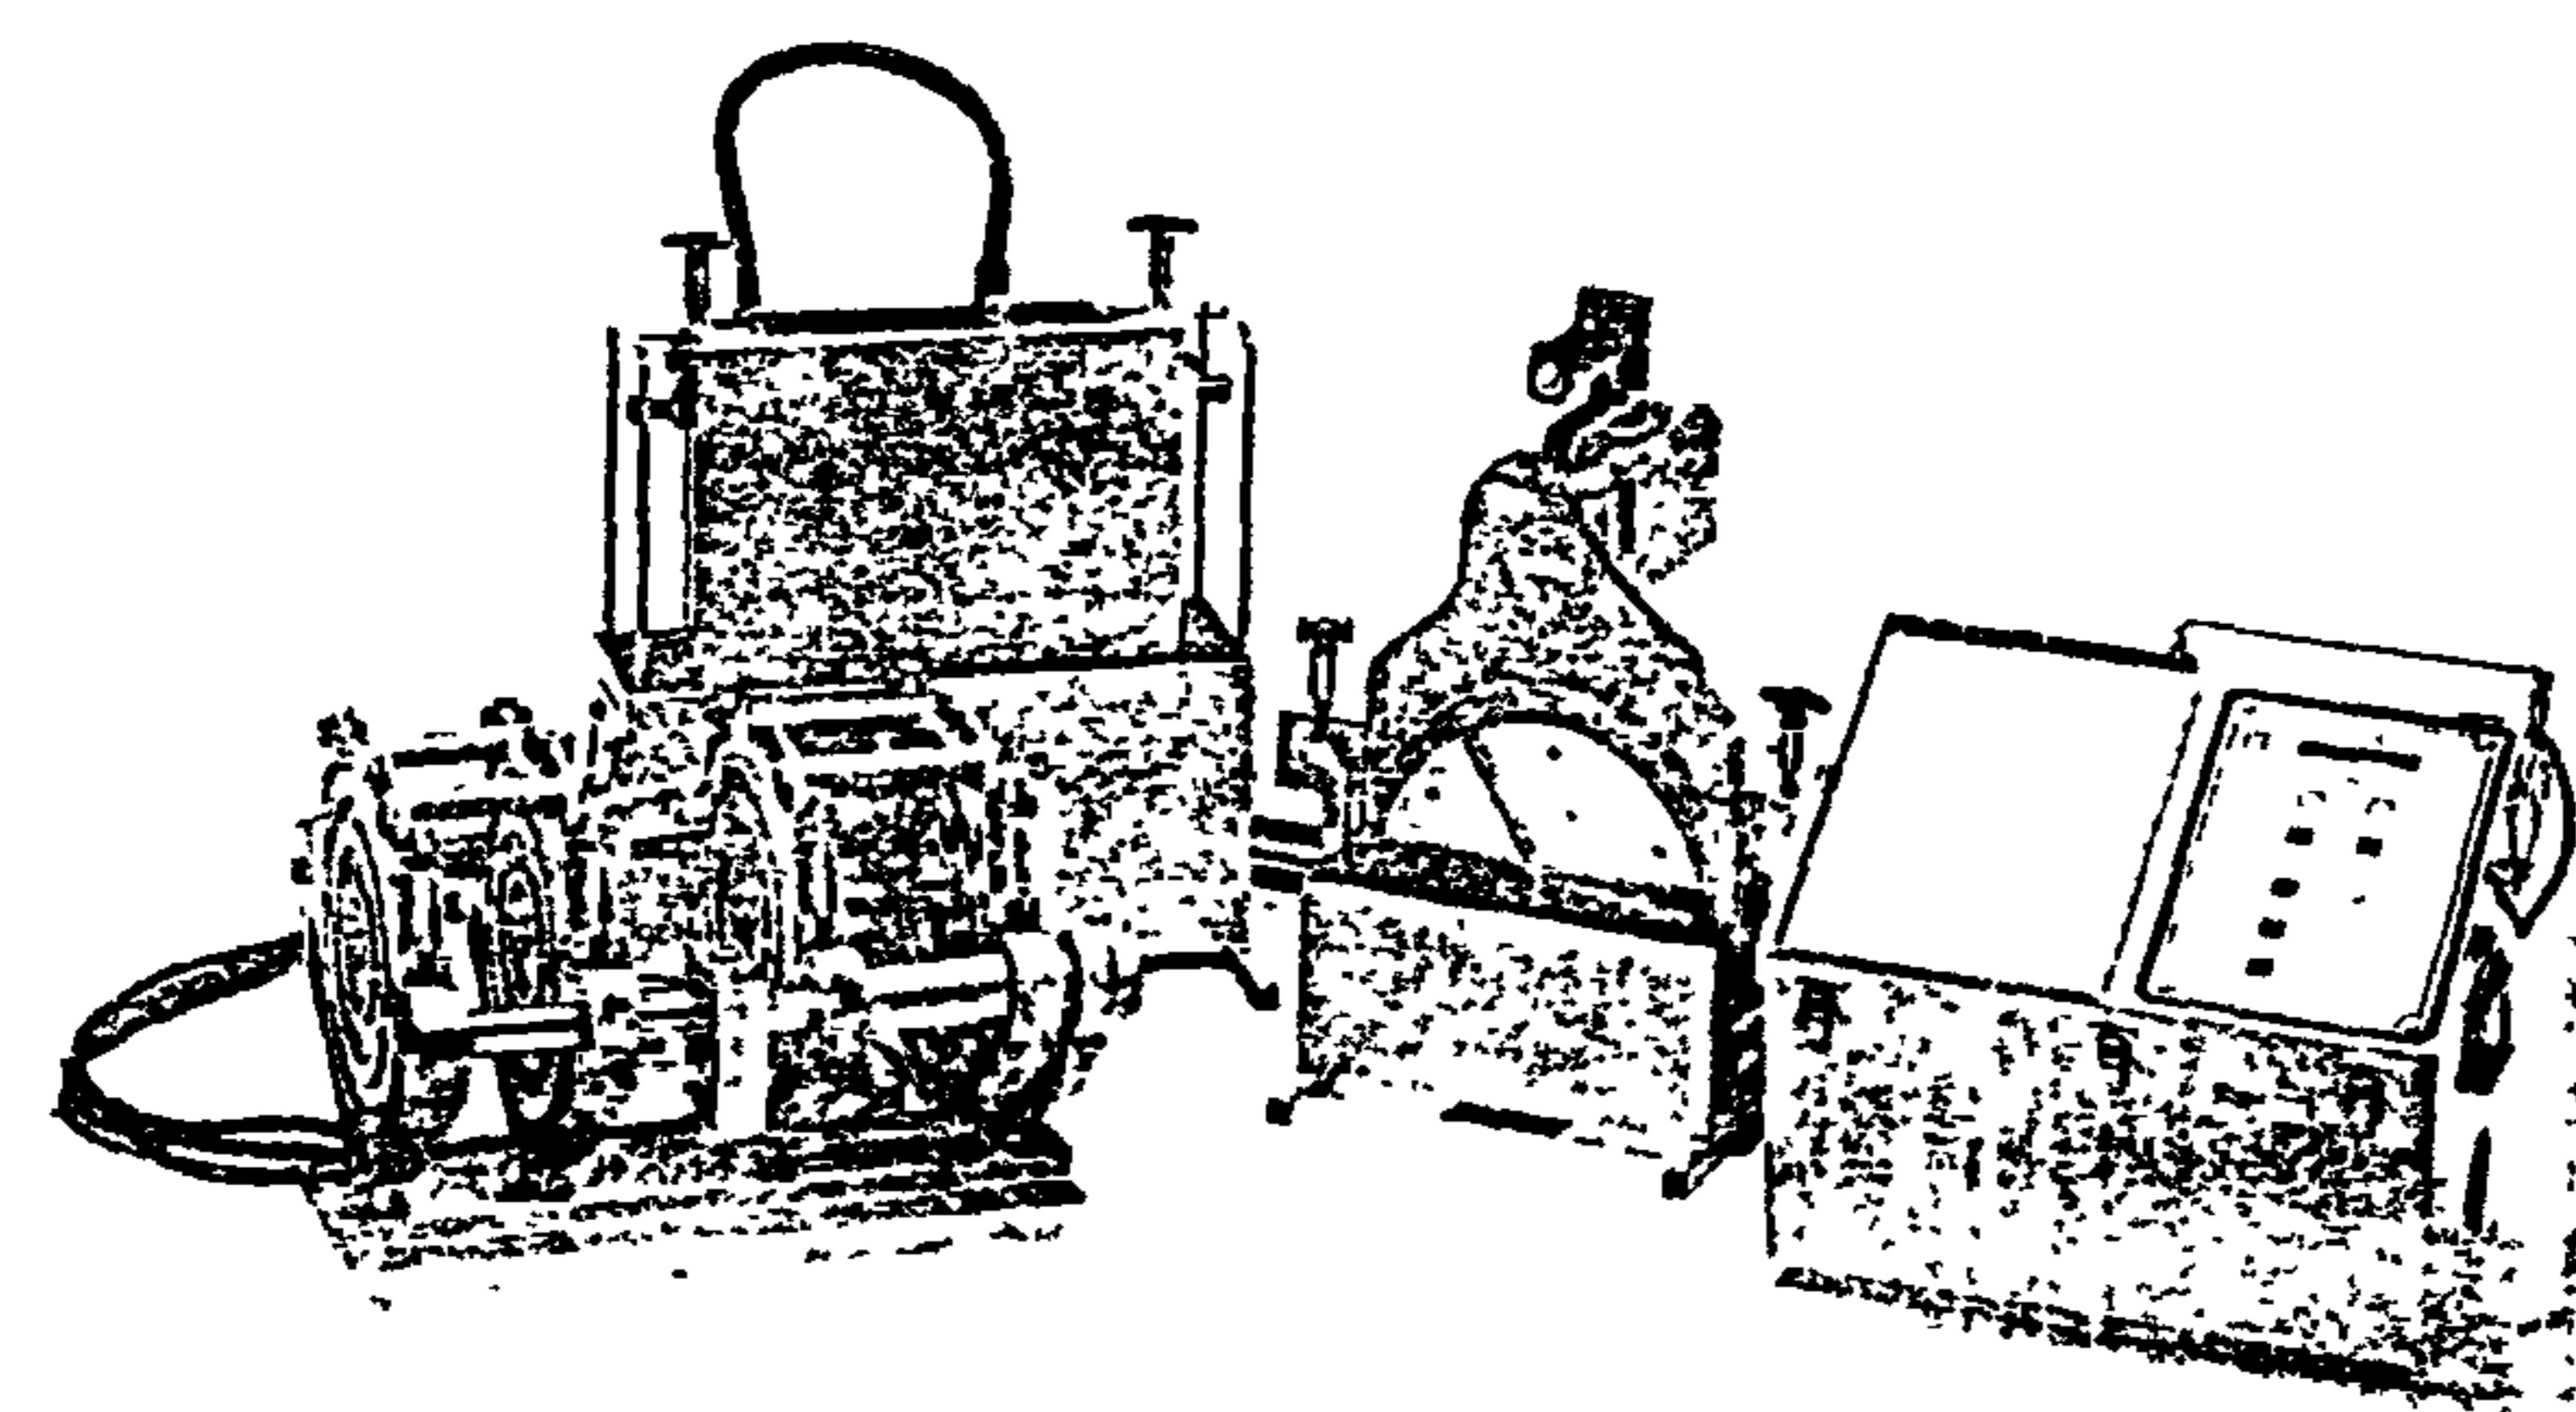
Установка для сварки нагретым инструментом встык
